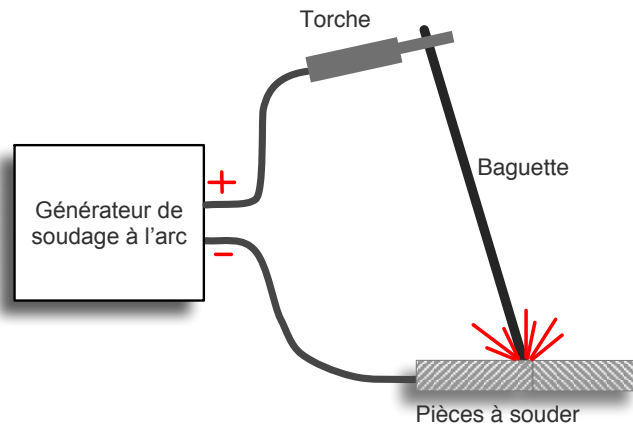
Schéma de principe du soudage manuel avec électrode enrobée
